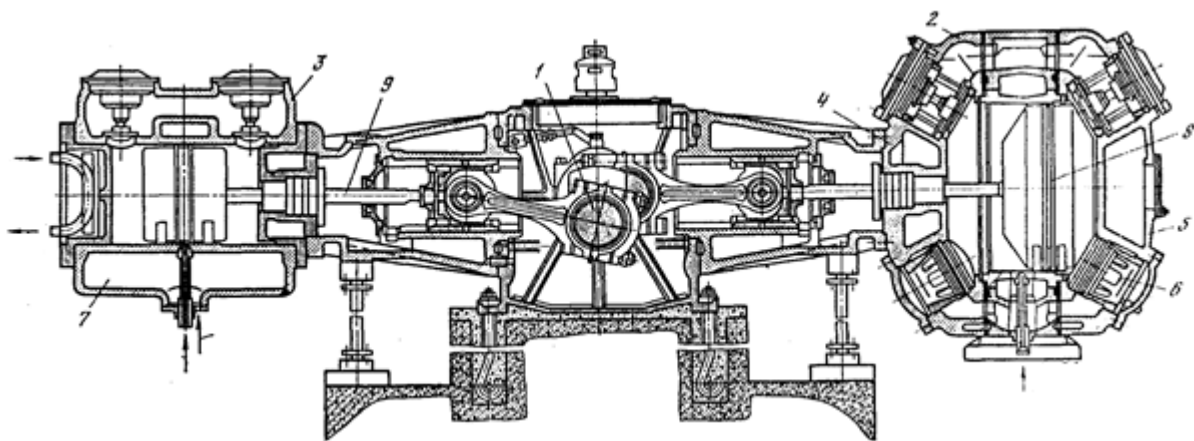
Повздовжній розріз компресора 4М10-100/8
